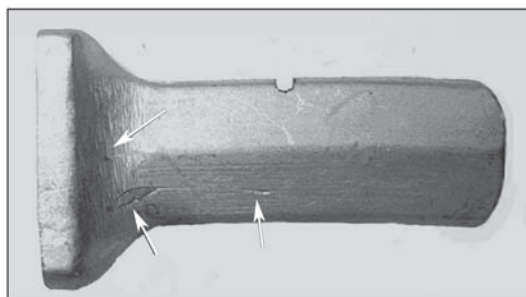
Дефекты в виде надиров и рисок на поверхности выдавленной заготовки
